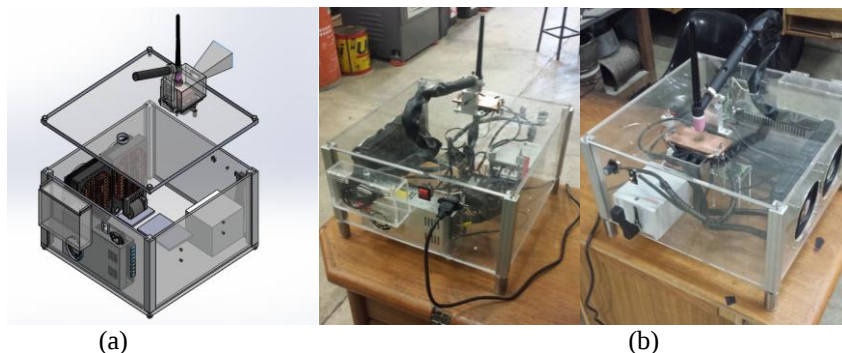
(a) Visão isométrica do equipamento (Projeto em SolidWorks®); (b) Equipamento construído
